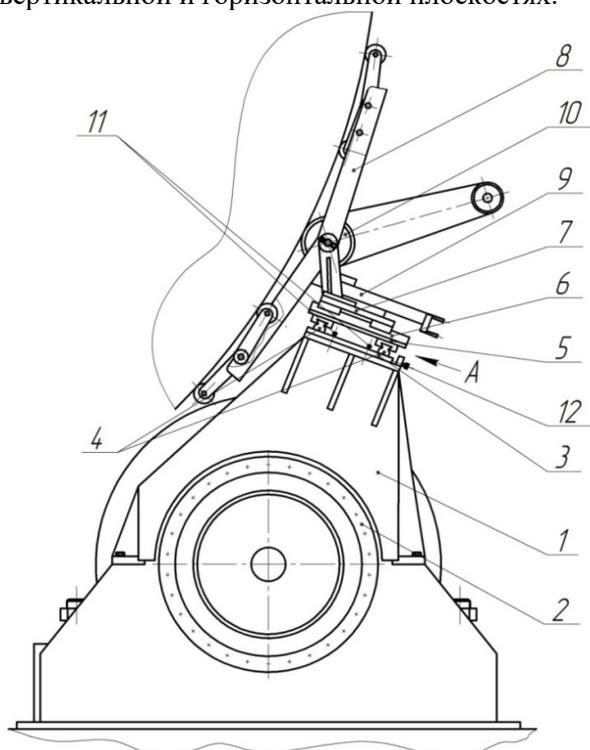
Облегченная конструкция ленточно-шлифовального станка
